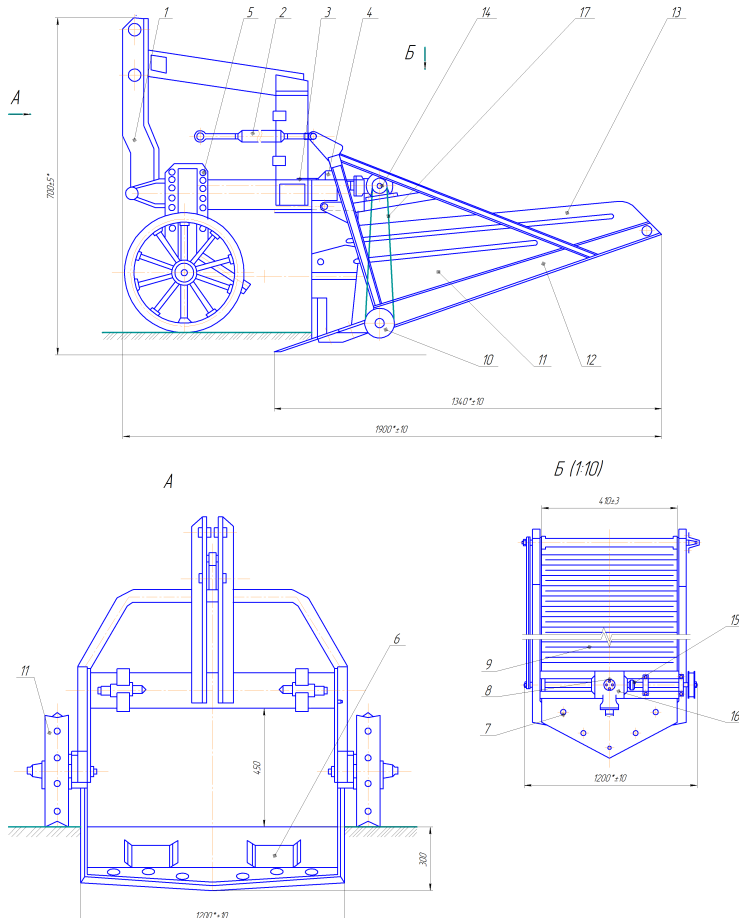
Схема розробленої скоби: 1 – начіпний механізм; 2 – тяга; 3 – карданний вал; 4 – захисний кожух; 5 – фіксатор; 6 – подовжувач; 7 – леміш; 8 – редуктор; 9 – елеватор ґрунту; 10 – ведений шків; 11 – опорне колесо; 12 – рама; 13 – захисний щит; 14 – ведучий шків; 15 – муфта втулкова; 16 – гідромотор; 17 – зубчатий пас
